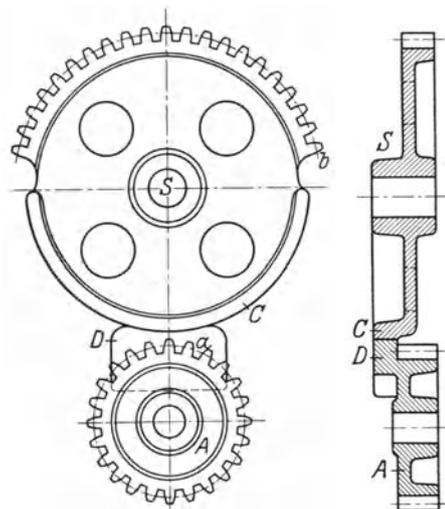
Getriebe zur Verhütung einer ungewollten Umsteuerung.
